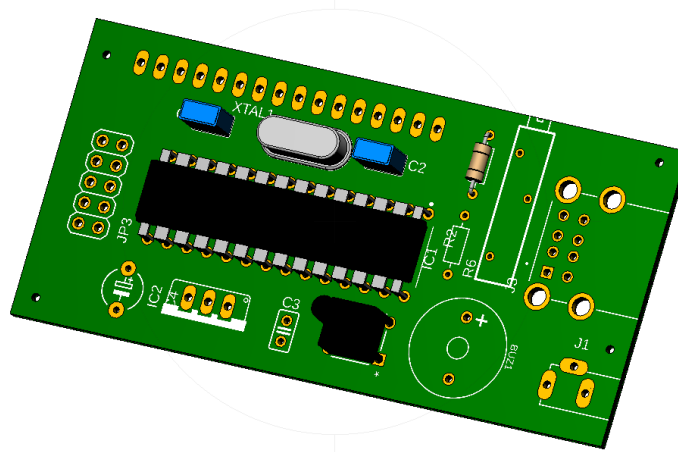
Conexión del microcontrolador ATmega328P en la PCB
